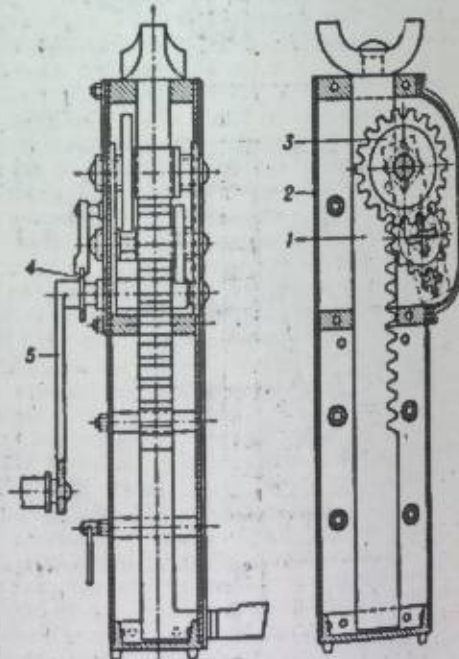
Реечный домкрат: 1 — зубчатая рейка; 2 — корпус; 3 — приводной механизм; 4 — храповое колесо; 5 — рукоятка.
